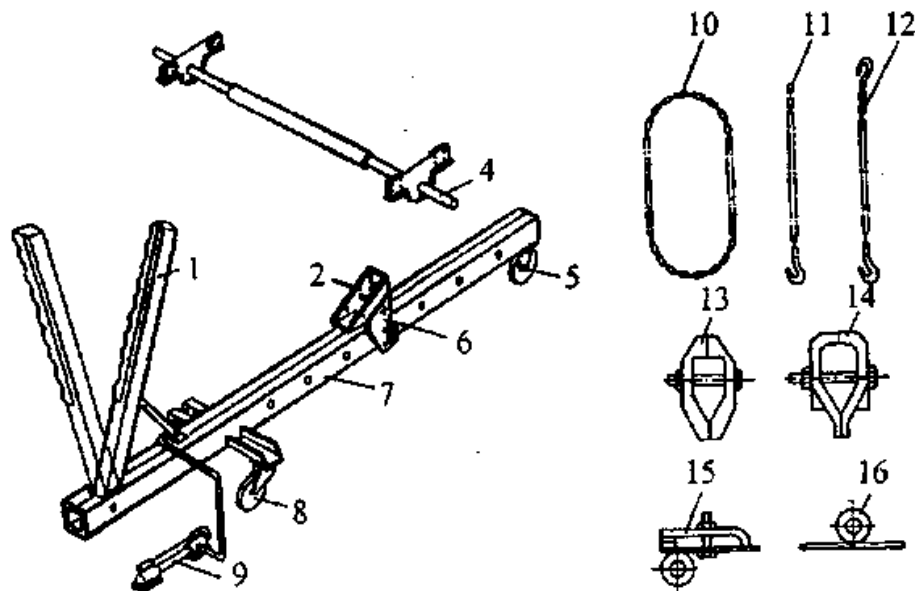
Пристрій БС-71 для правки кузовів:
